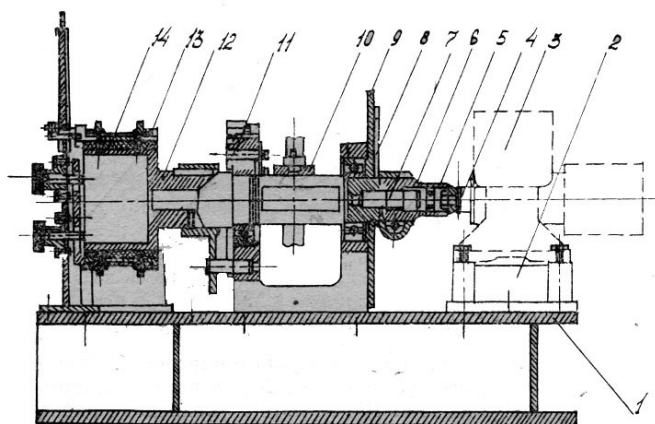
схема приспособления стенда для обработки рулевой машинки:
